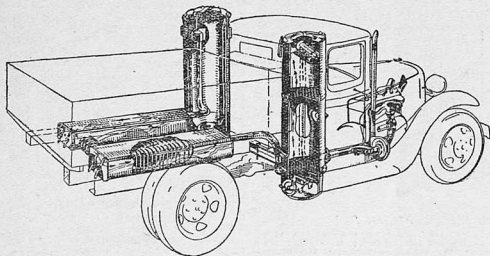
Расположение агрегатов газогенераторной установки НАТИ Г-14 на шасси автомобиля
